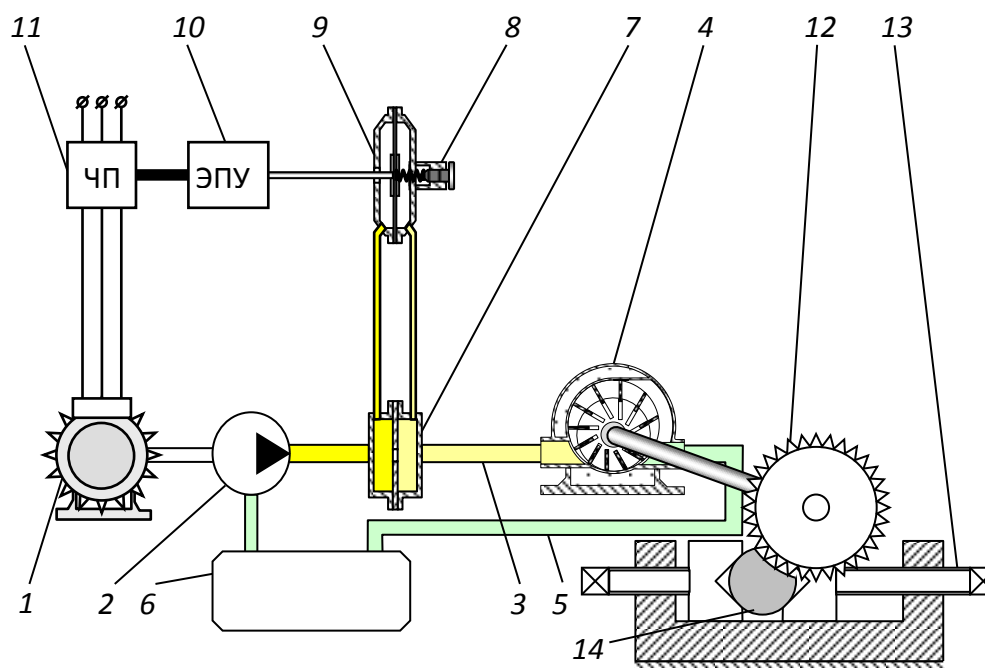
Схема привода дисковой пилы в отрезных станках гидроприводом:
